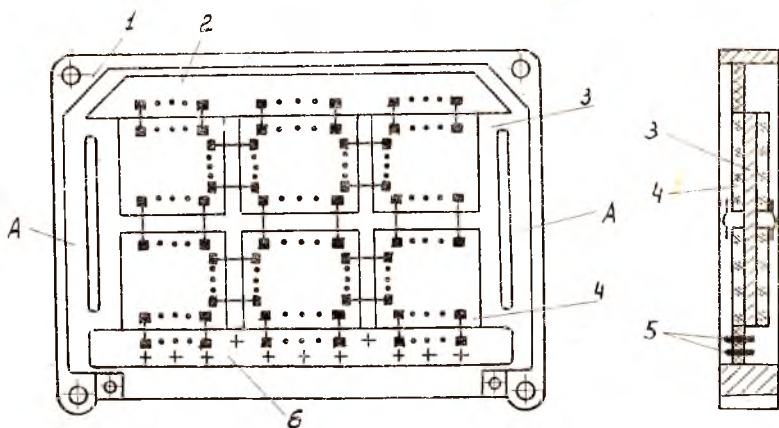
Двусторонняя ячейка герметичного блока МЭА на металлической рамке: 1 — рамка; 2 и 6 — верхняя и нижняя печатные вставки; 3 — планка рамки; 4 — бескорпусная микросборка; 5 — штыри
